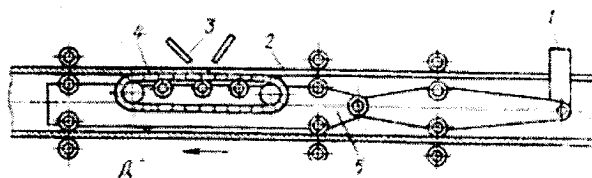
Схема зварювання зовнішнього шва труби.
